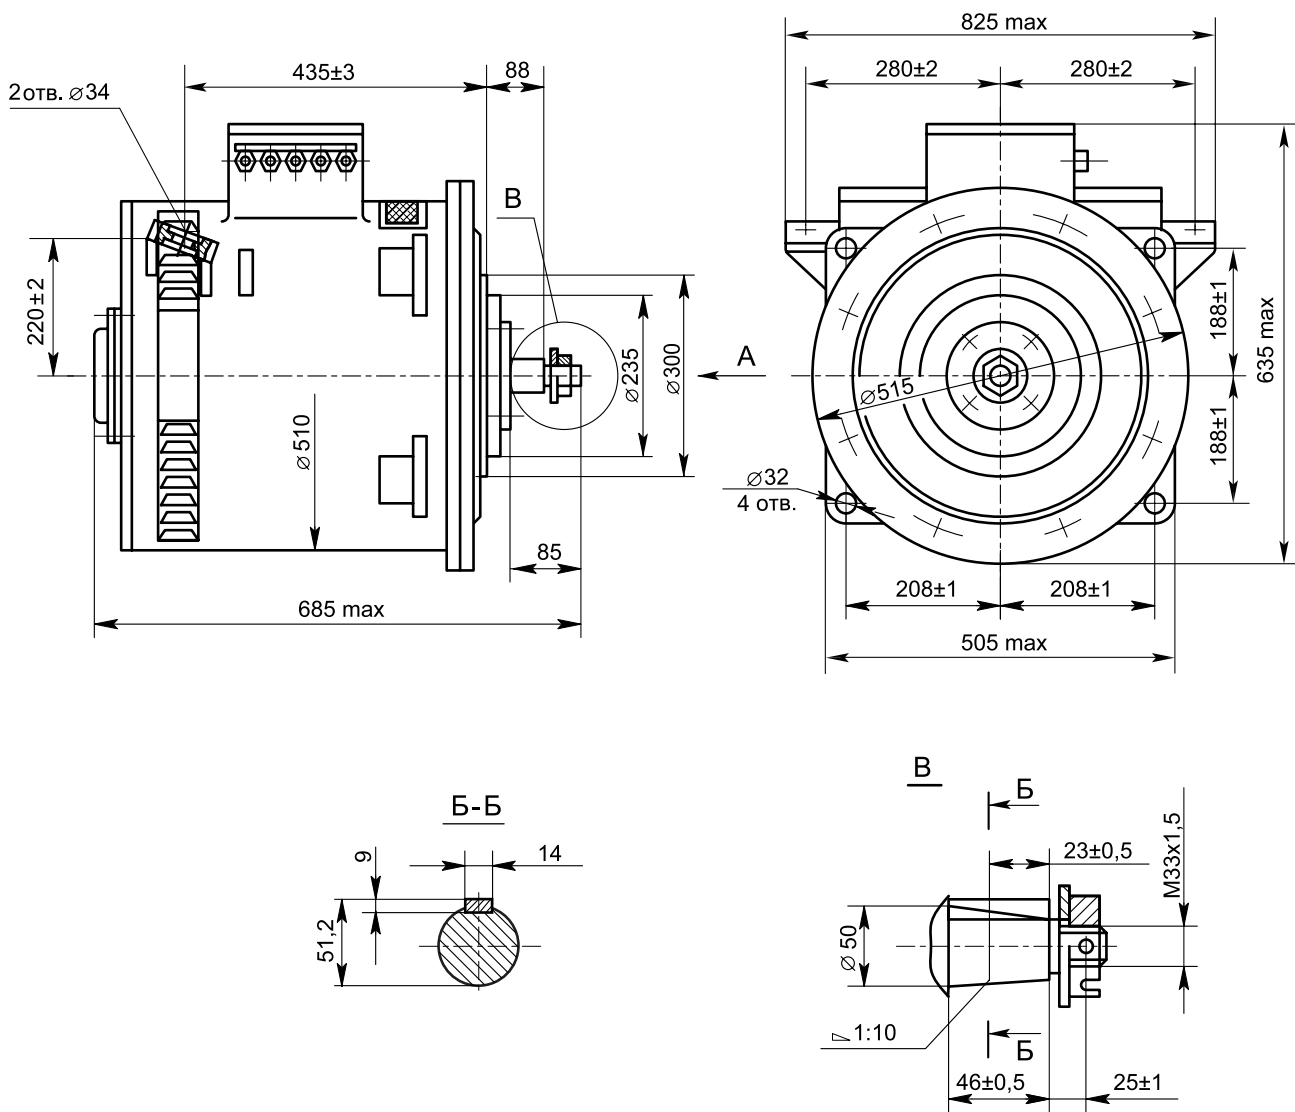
Габаритные и установочные размеры электродвигателя ДТН-34/25М
